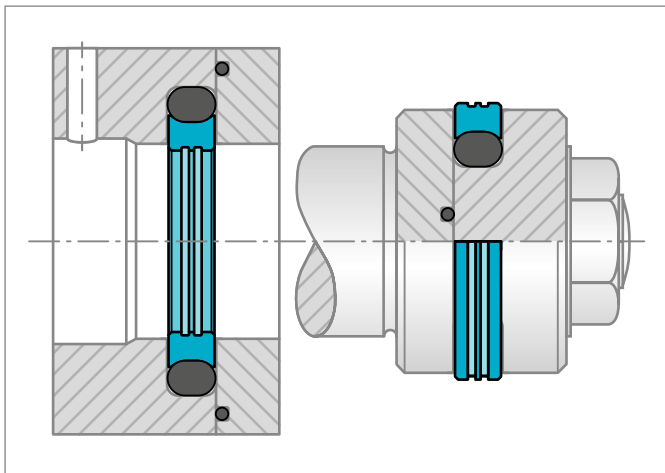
Einbau des Turcon® Roto Glyd Ring® in geteilte Nut
